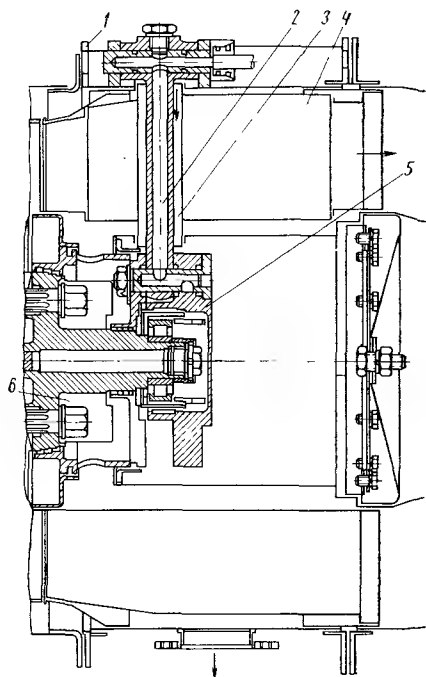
Крепление корпуса подшипника ГТУ «Пэлост» фирмы Блекборн
